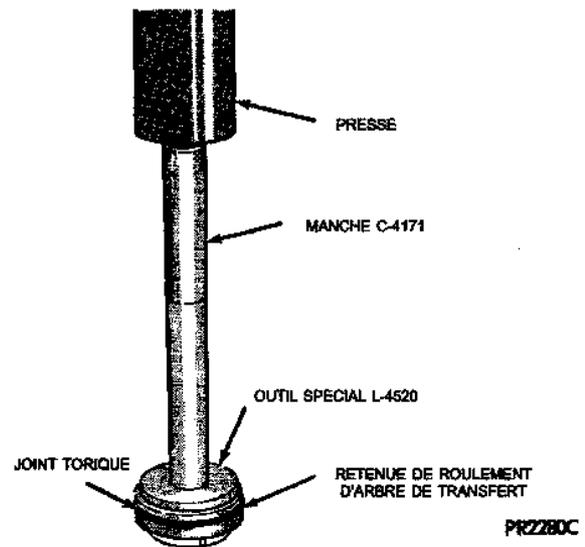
Pose de la cuvette de roulement d'arbre de transfert
